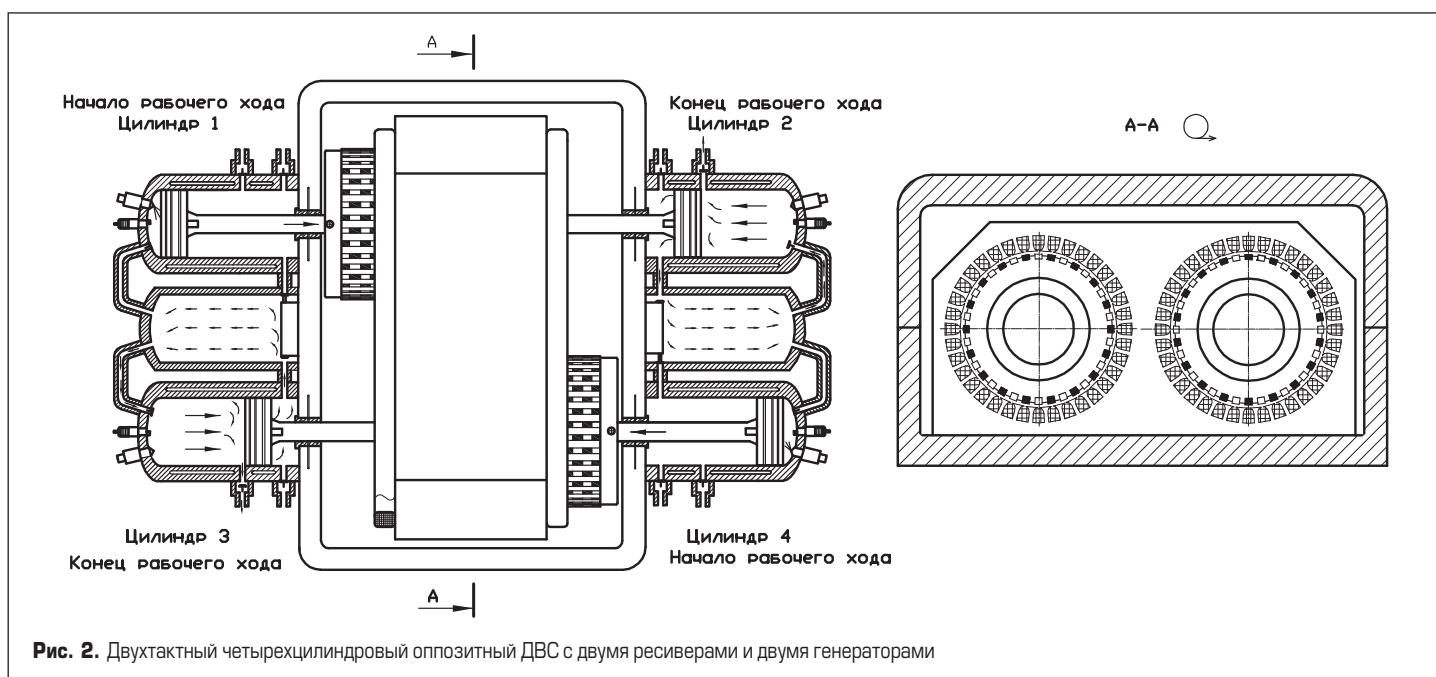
Двухтактный четырехцилиндровый оппозитный ДВС с двумя ресиверами и двумя генераторами
